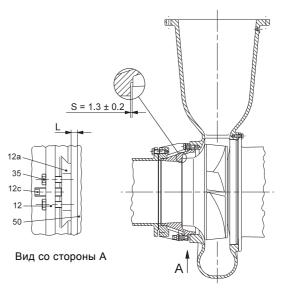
Зазор рабочего колеса, тип установки D и H, метод 2
